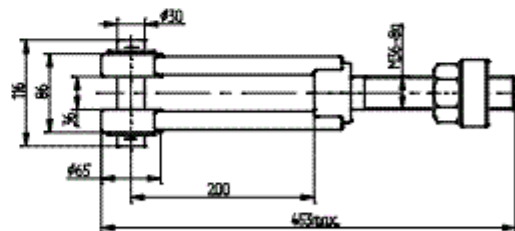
Соединительная тяга для механизмов М30-10000-97К (в комплекте - вилка и шток)
